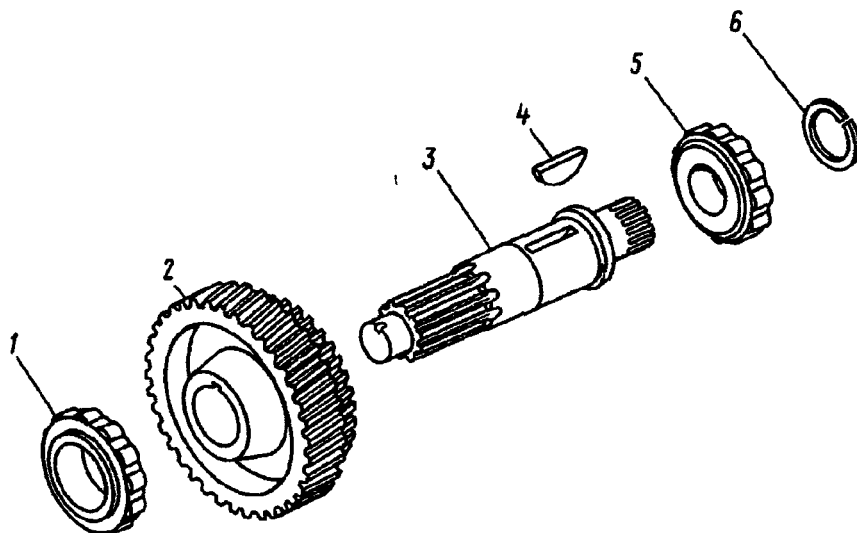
Вал И801.25.000 ведущий раздаточной коробки:
